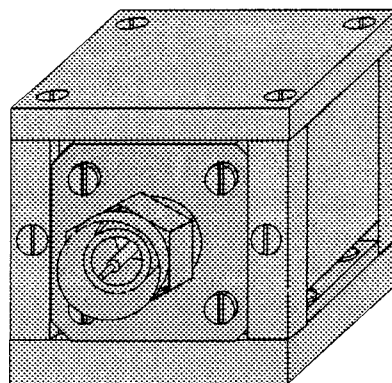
Cellule complètement assemblée et fermée par le couvercle
